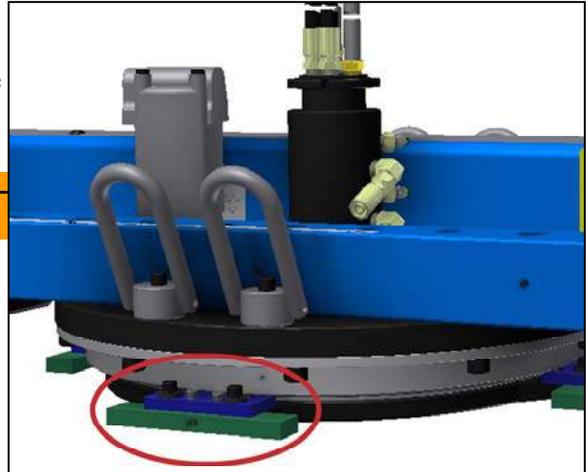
ASSEMBLAGE DU KIT DE MONTAGE EN SURFACE
